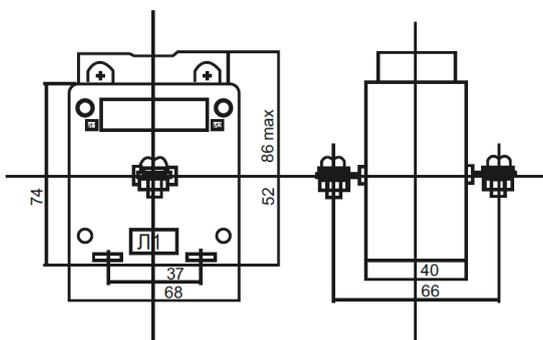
Габаритные и установочные размеры трансформаторов тока ТШП-0,66
